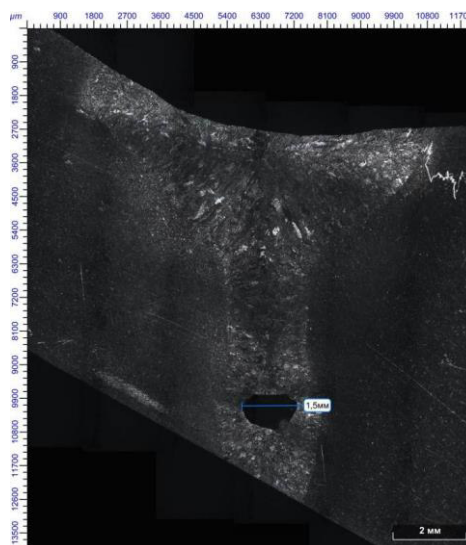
Пора в нижней части сварного шва стали 06X15H6MBФБ-Ш
